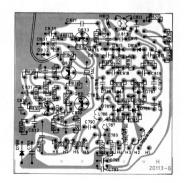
Demodulatorplate (plate H) sett fra foliesiden.
